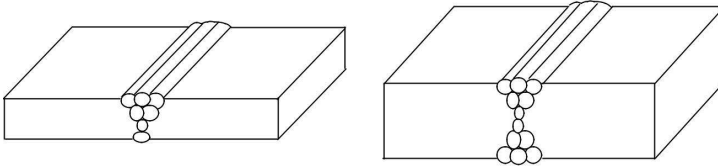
Формування швів при зварюванні пластмасових деталей
